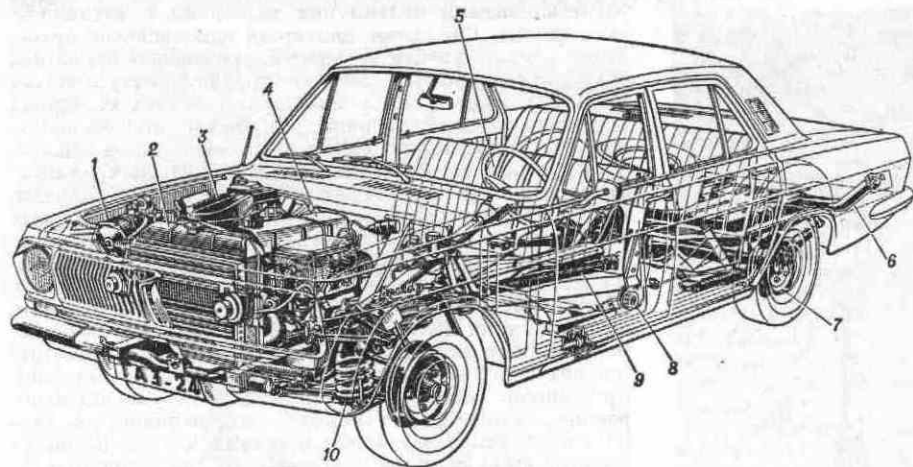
Элементы автомобиля «Волга» ГАЗ-24: 1 — гидровакуумный усилитель тормозов; 2 — радиатор; 3 — воздушный фильтр карбюратора; 4 — двигатель; 5 — рулевое управление; 6 — топливный бак; 7 — тормоза; 8 — сиденье; 9 — карданный вал; 10 — передняя подвеска.
